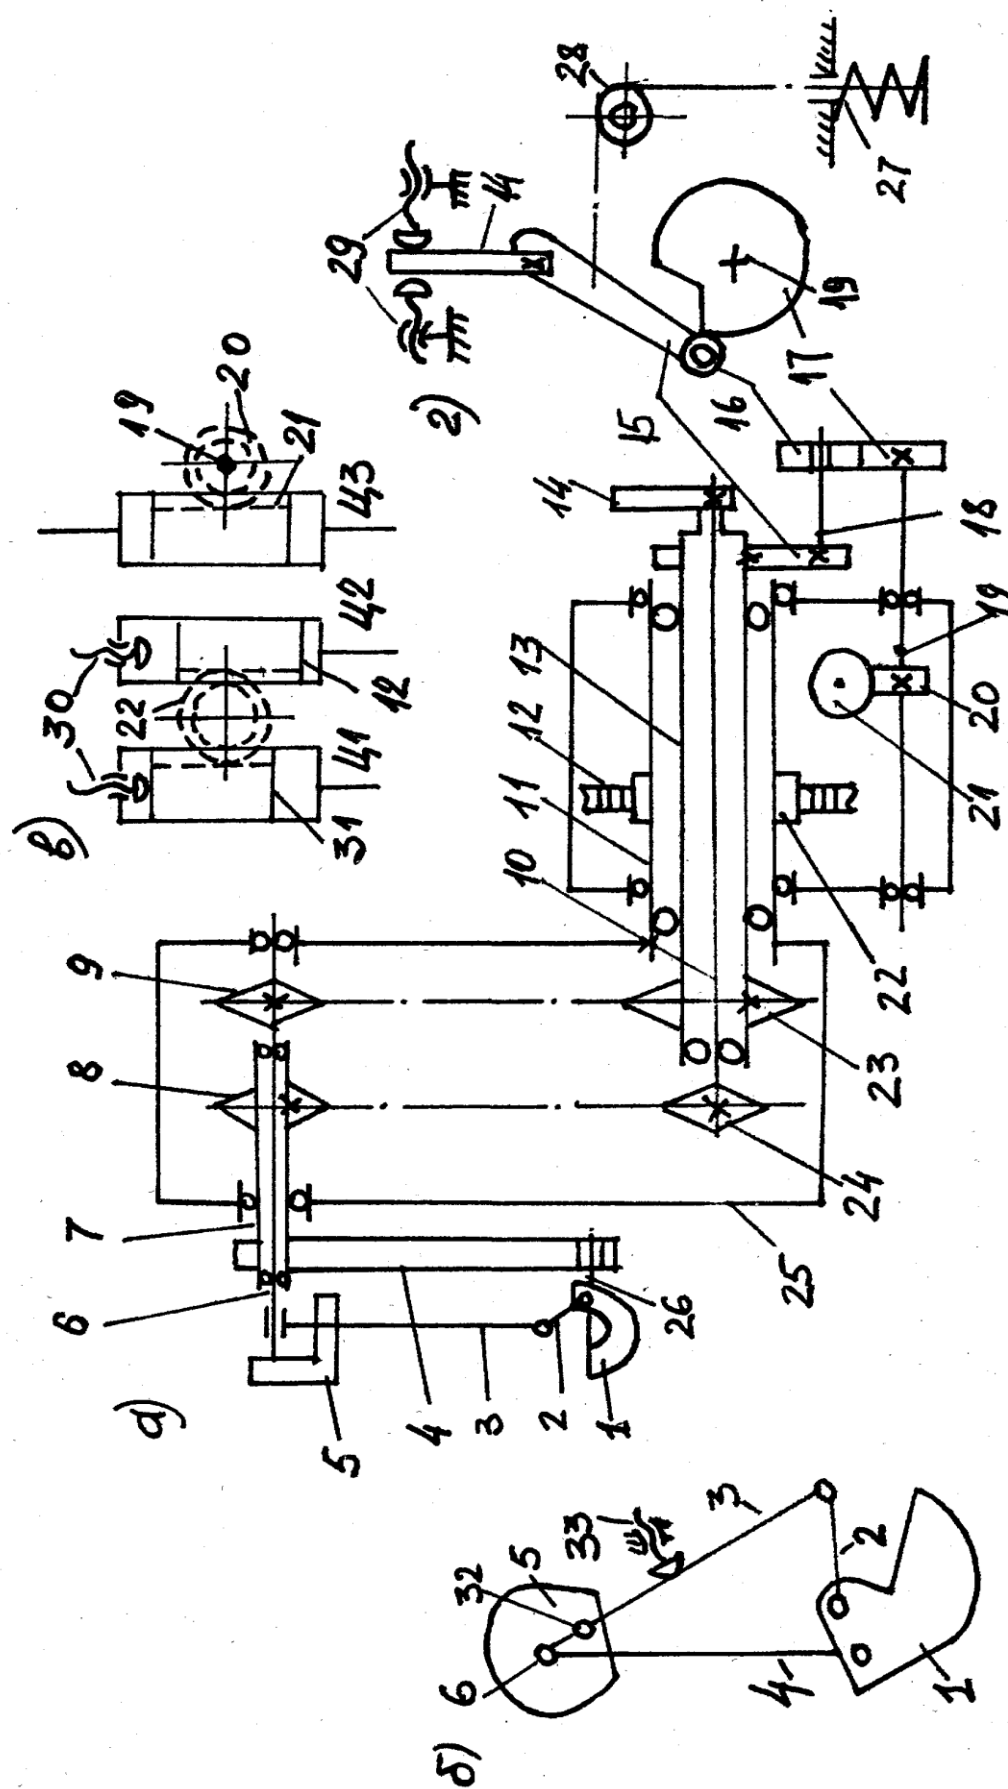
Кинематическая схема манипулятора для заливки металла
